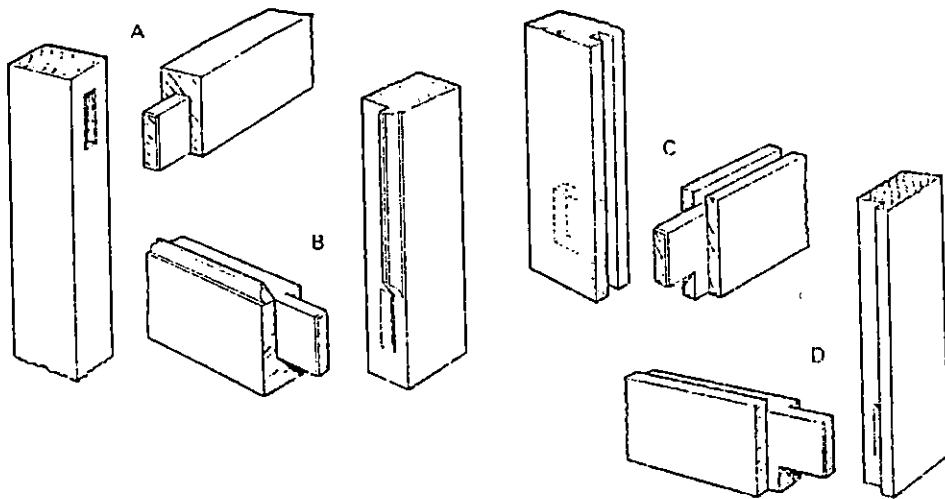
Ensamblajes de caja y espiga para puertas: A ensamble de caja y espiga sencillo para marco de bordes escuadrados; B marco con moldura maciza cortada a inglete;
